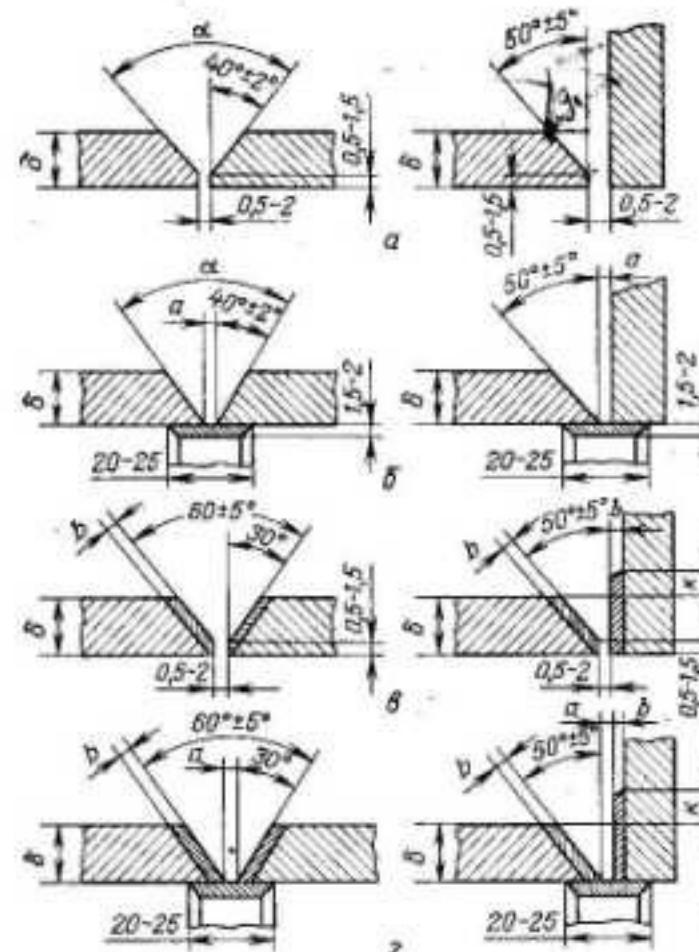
Подготовка кромок и сборка под сварку кольцевых угловых соединений:
